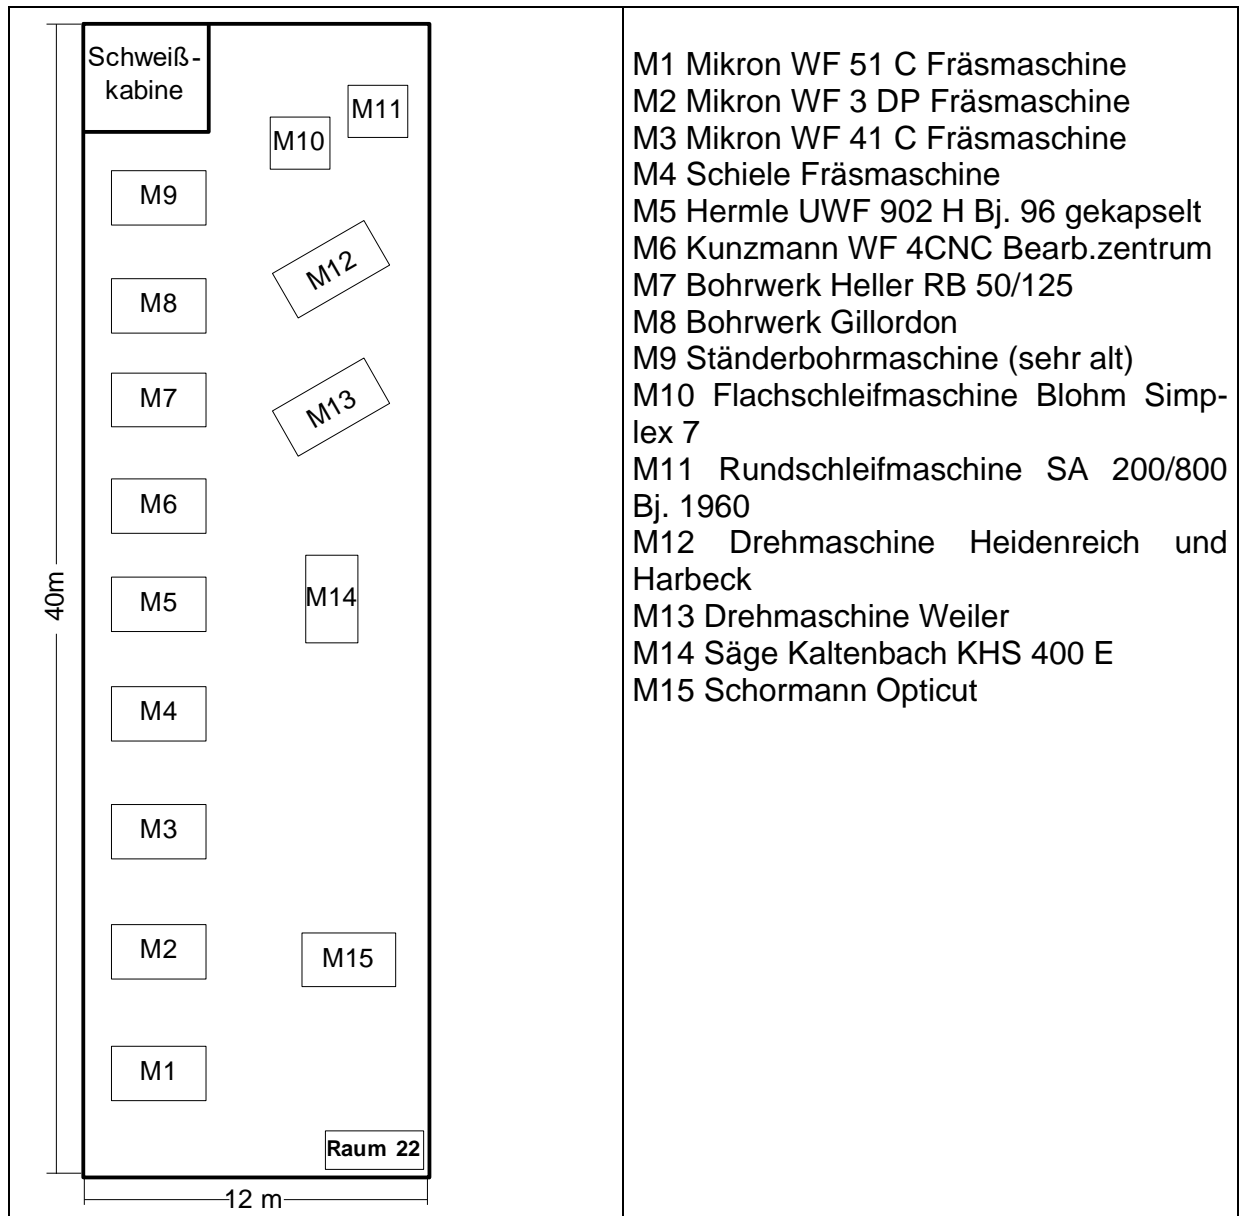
Grundriss der Fertigungswerkstatt und Maschinenbelegung
